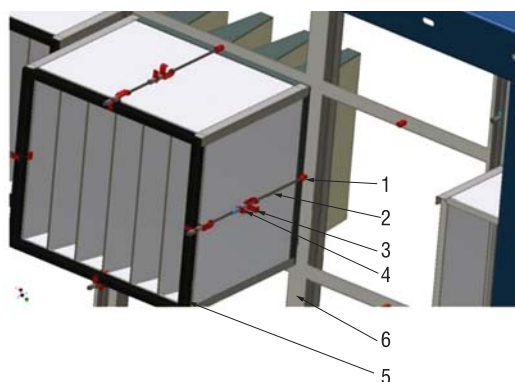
Крепление рамки фильтрующего модуля с элементами ФГО:
